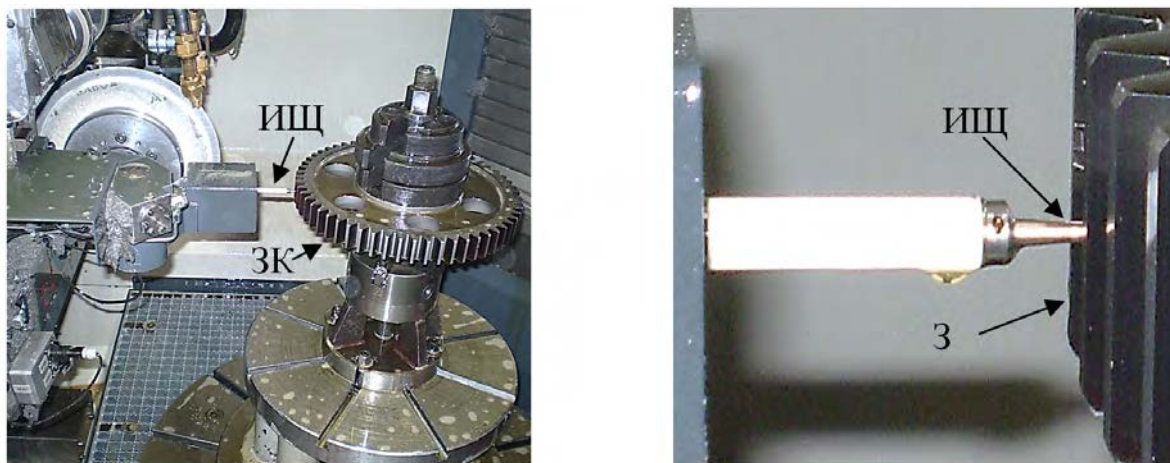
Общий вид (слева) и зона измерения (справа) припуска измерительным щупом компании Renishaw на станке HOFLER RAPID 1250: ИЩ – измерительный щуп; ЗК – зубчатое колесо
